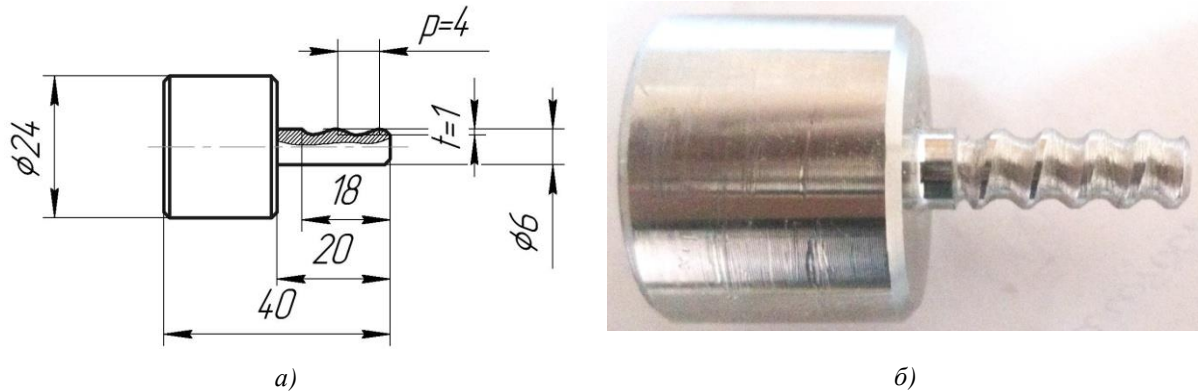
Металеві вставки круглої зовнішньої різьби: а) ескіз металевої вставки; б) фото вставки
